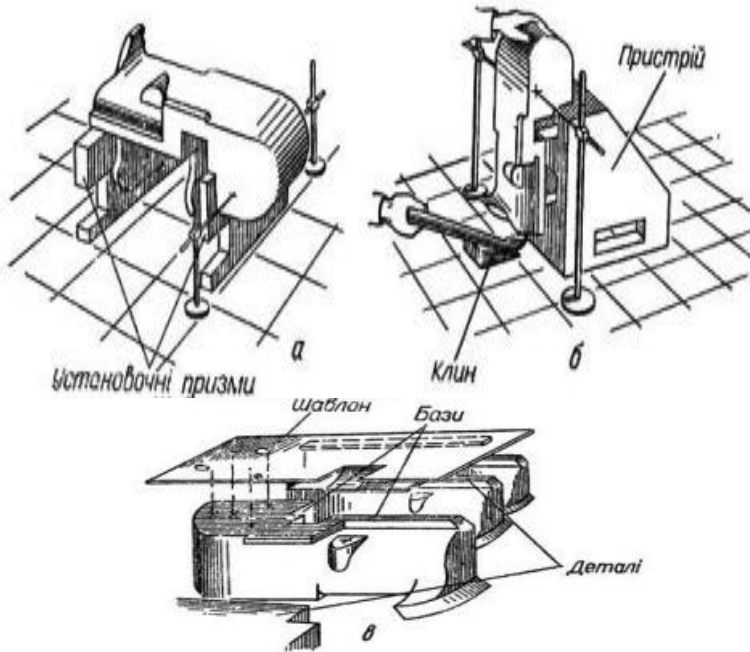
Розмічання корпусу коробки за допомогою: а – установочних призм; б – спеціального пристрою; в – просторового (об’ємного) шаблону
